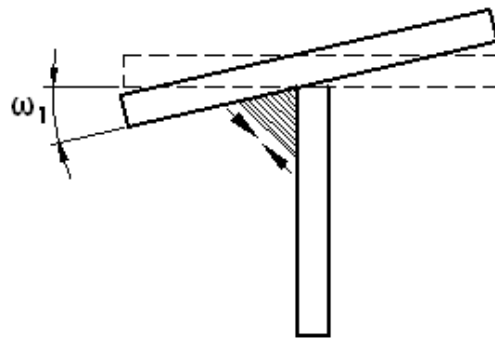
Distorsión angular producida por la contracción del cordón de soldadura
